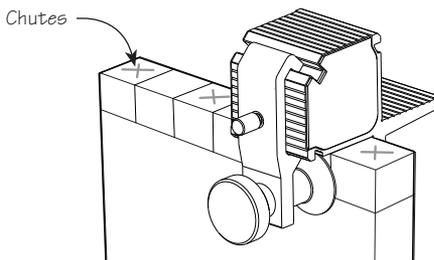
Guide de sciage prêt pour la coupe d'une queue.
